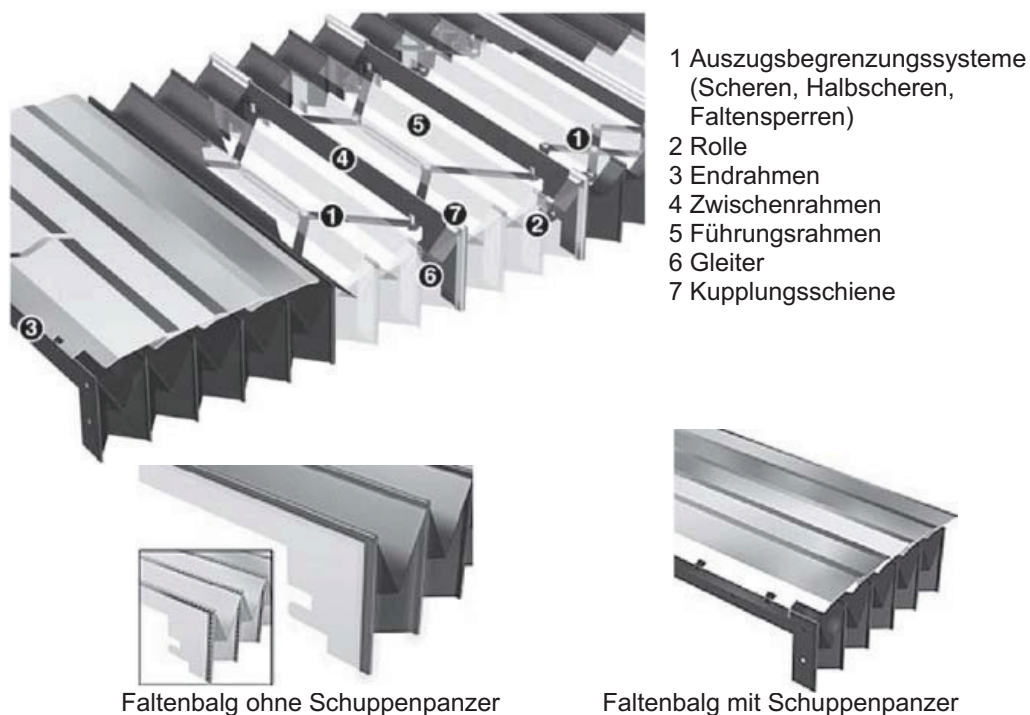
Teleskopabdeckung einer Werkzeugmaschine. Quelle: Hennig
